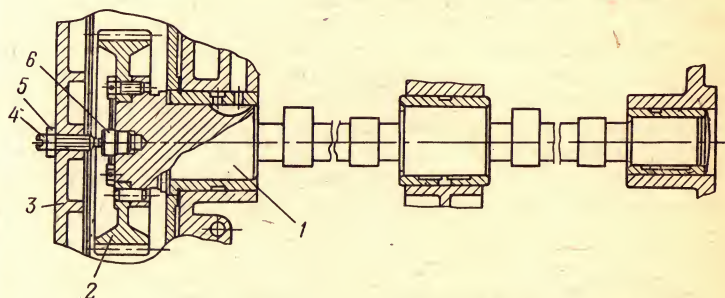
Схема регулировки осевого смещения распределительного вала двигателя СМД-14:
